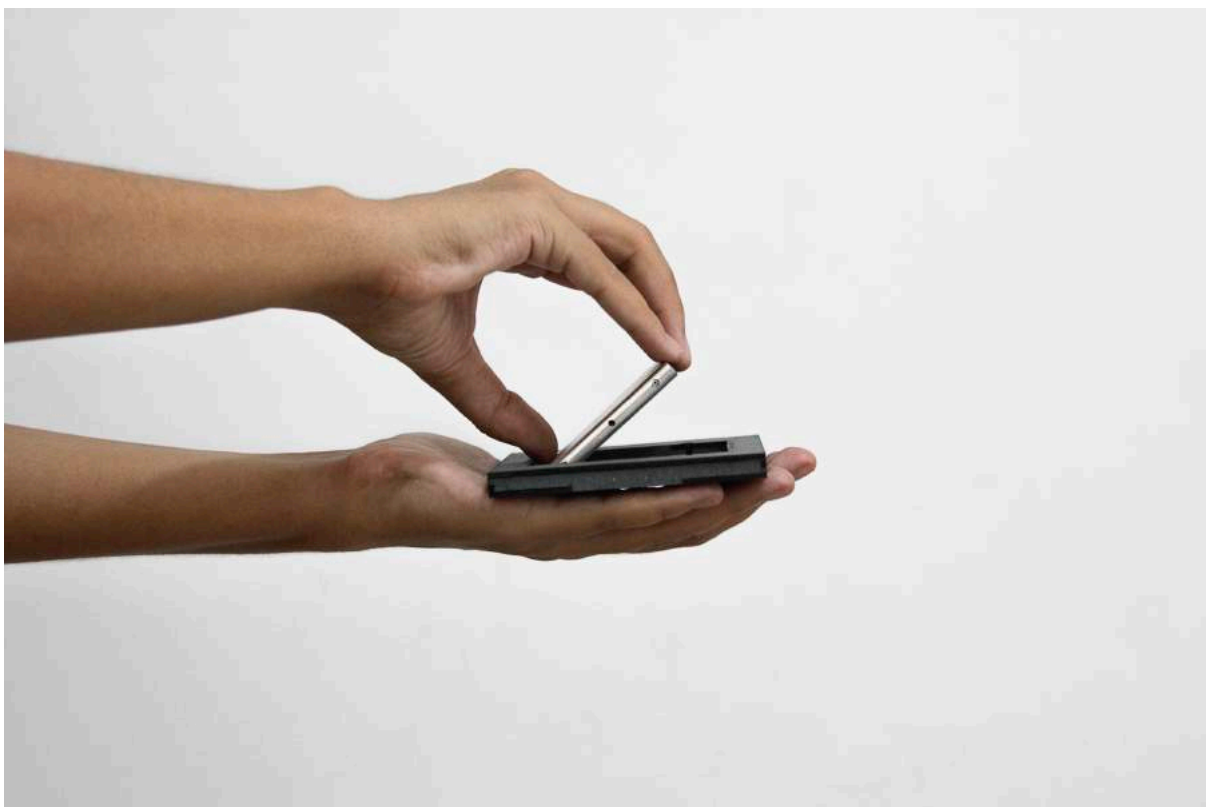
Joia sendo destacada da cama. Fonte: Acervo da autora.
